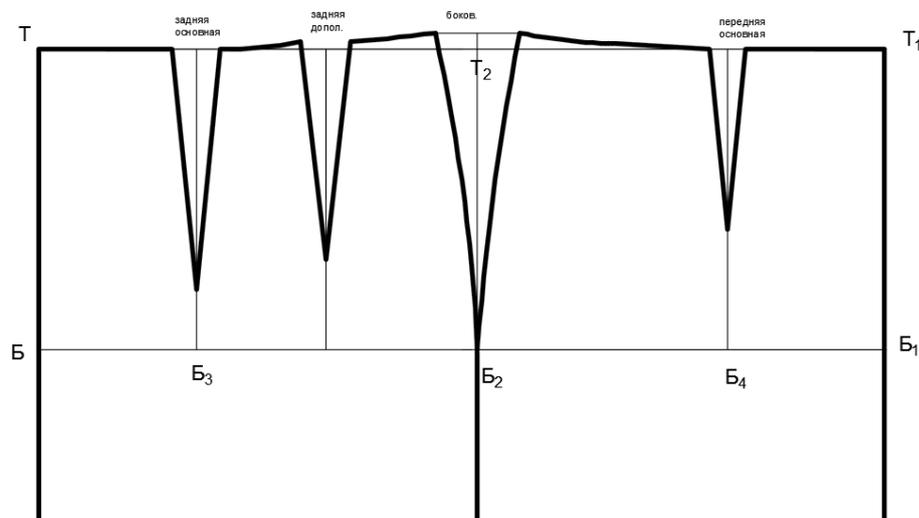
Схема чертежа конструкции юбки с двумя вытачками сзади (фигура с выступающими ягодицами)
